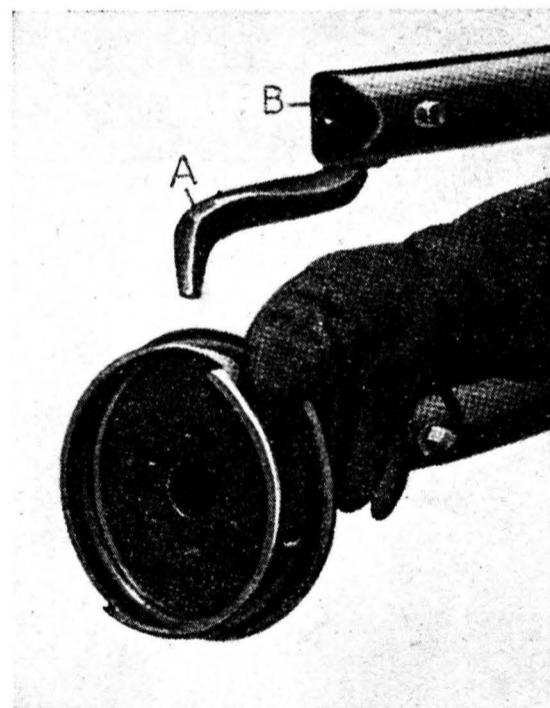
Verschweißung des Deckels mit dem Auszieher durch Punktschweißung.
